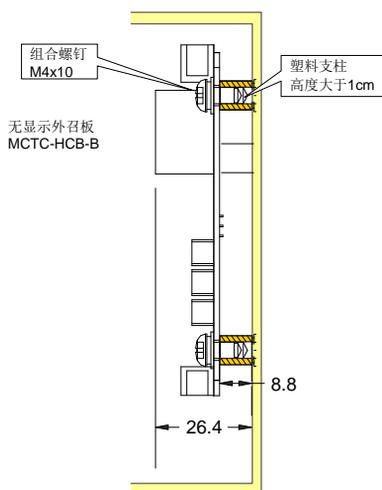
HCB-B 外观、尺寸及安装示意图 (单位: mm)
